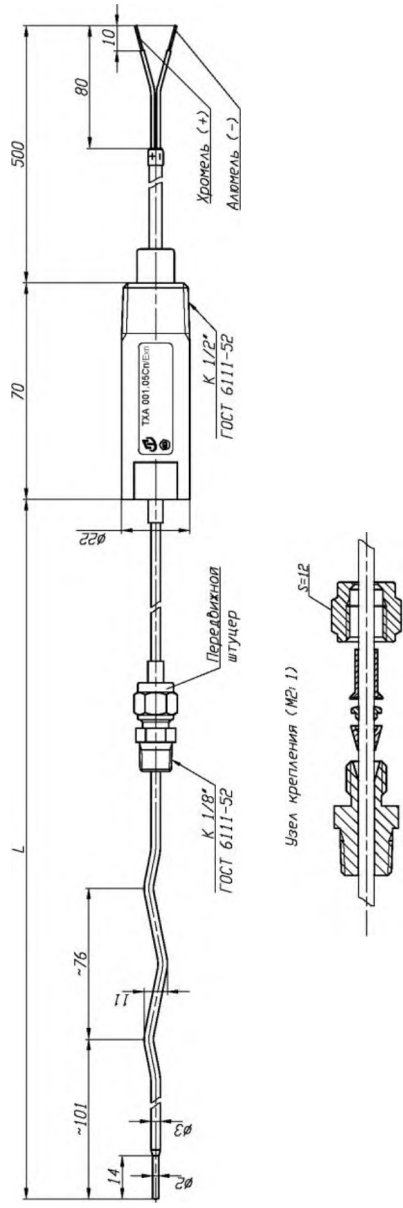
5 б) – Габаритный чертёж ПТ модели ТХА 001.050Сп-Ехп
